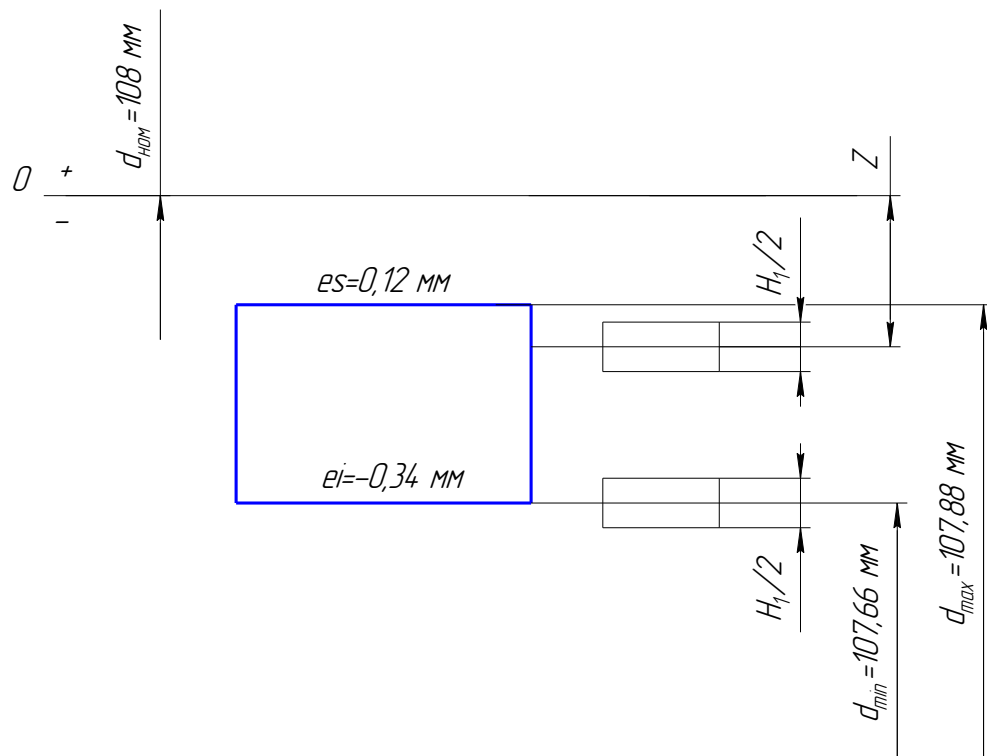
Схема розташування допусків робочих поверхонь скоби для контролю розміра $\varnothing 108d11\left(\begin{smallmatrix} -0,12 \\ -0,34 \end{smallmatrix}\right)$
